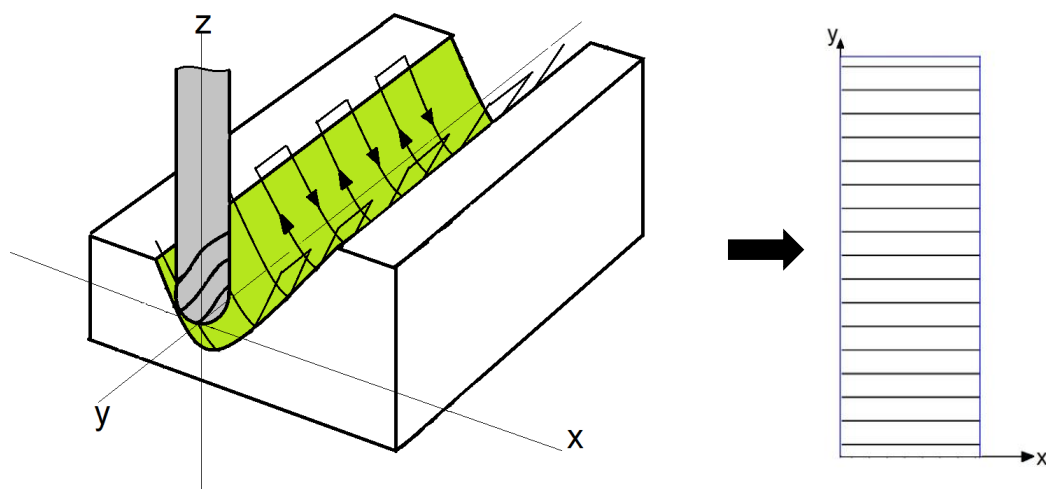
Схема фрезерования с траекторией, расположенной поперек формообразующей поверхности
